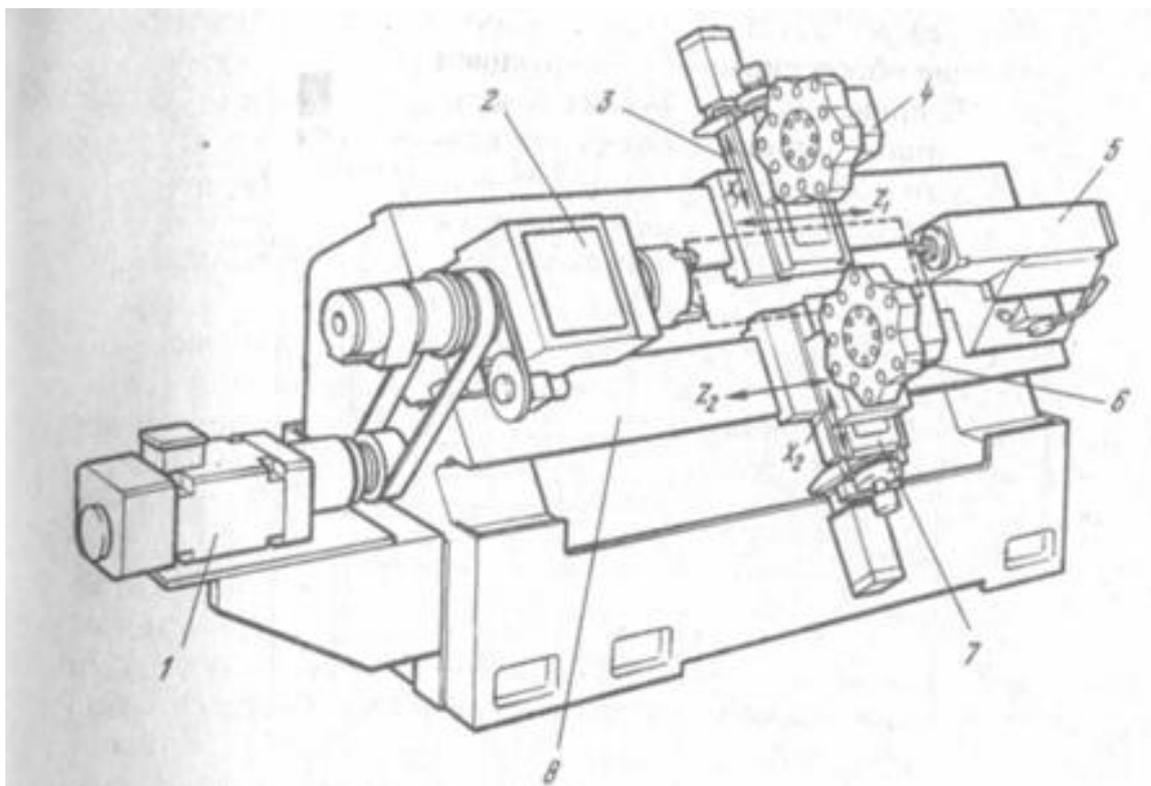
Наклонная компоновка токарного станка с ЧПУ.
